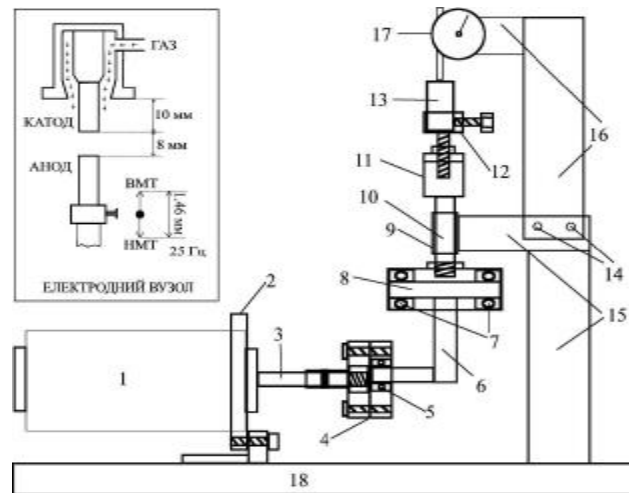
Схема електродного вузла та електромеханічного модулятора зі встановленим індикатором годинникового типу для вимірювання амплітуди коливань: 1 — двигун; 2 — фланець; 3 — вал двигуна; 4 — муфта; 5 — вальниця кочення; 6 — шатун; 7 — вальниця кочення; 8 — вісь; 9 — напрямна втулка штока; 10 — шток; 11 — гайка для регулювання висоти електрода; 12 — тримач електрода; 13 — електрод; 14 — кріплення кронштейна; 15 — стійка; 16 — кронштейн; 17 — індикатор годинникового типу; 18 — основа.
